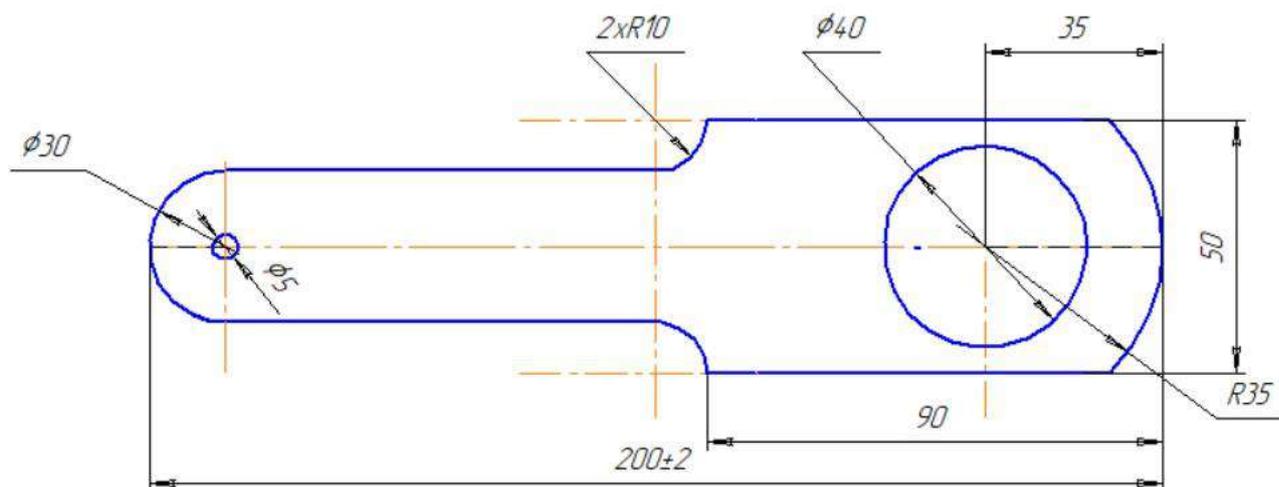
Чертеж ракетки для игры «Бильбоке»
